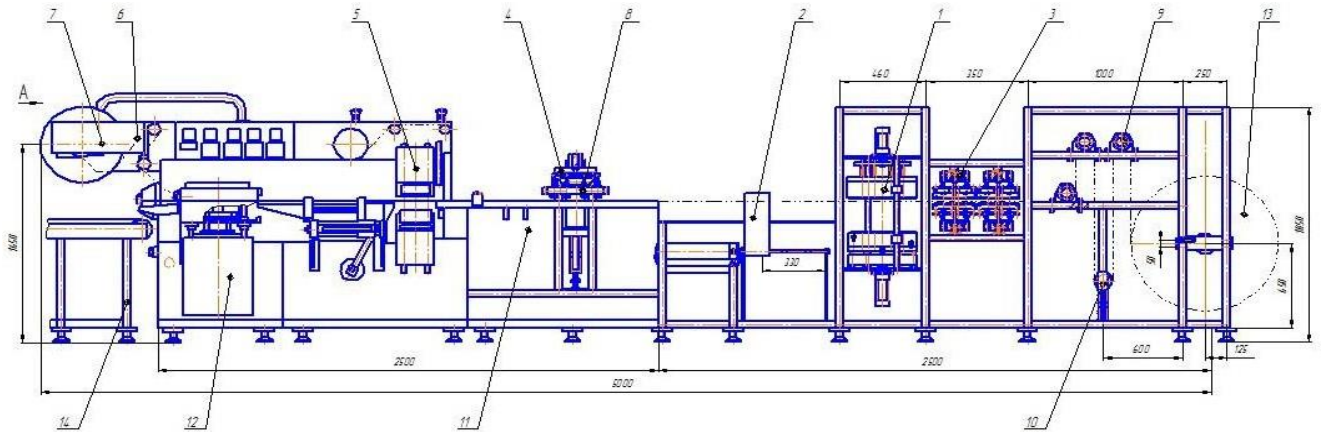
1 - камера термоформування; 2 - механізм протягування стрічки; 3 - механізм нагрівання; 4 - дозатор; 5 - пристрій для заклеювання; 6 - механізм змотування відходів; 7 - привод змотування відходів; 8 - дозувальна головка; 9 - нерухомі натяжні ролики; 10 - рухомий натяжний ролик; 11 - контролюючий пристрій; 12 - відрубний прес; 13 - рулон зполоістиролом; 14 - відвідний конвеєр.
